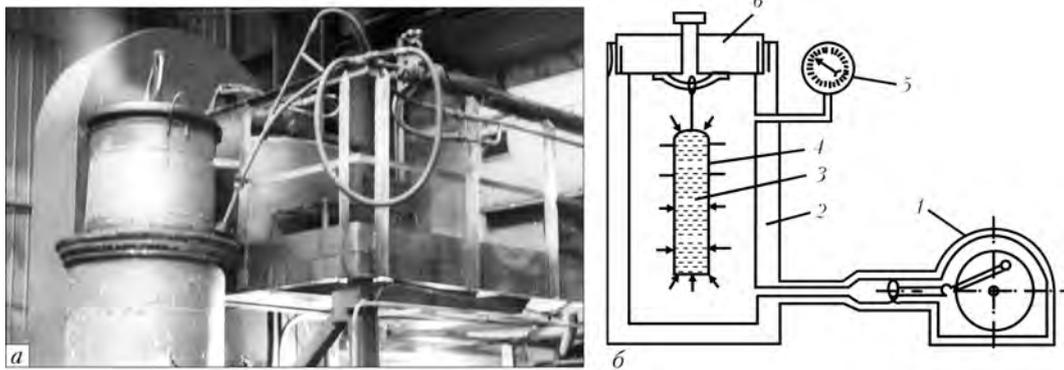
Установка холодного изостатического прессования: *a* — внешний вид; *б* — схема; 1 — насос высокого давления; 2 — камера; 3 — титановая губка; 4 — эластичная оболочка; 5 — манометр; 6 — крышка
